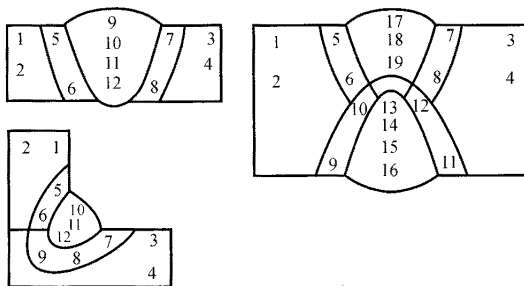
Схемы порядка замеров твердости на участках сварного соединения
